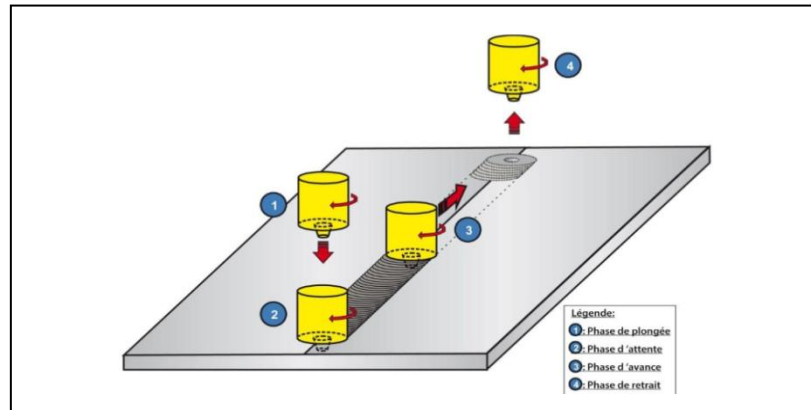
Représentation des étapes du soudage par friction-malaxage (FSW). [5]
